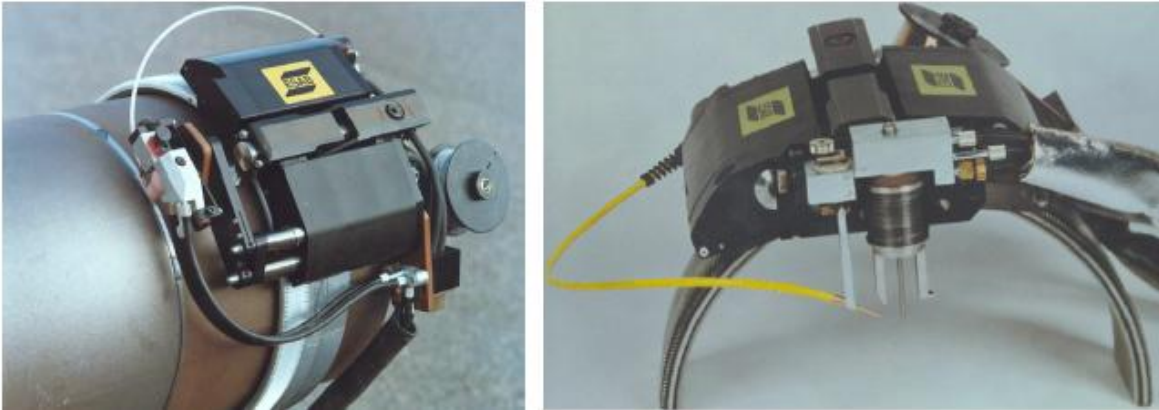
Sistema de robot para soldadura orbital de tuberías
